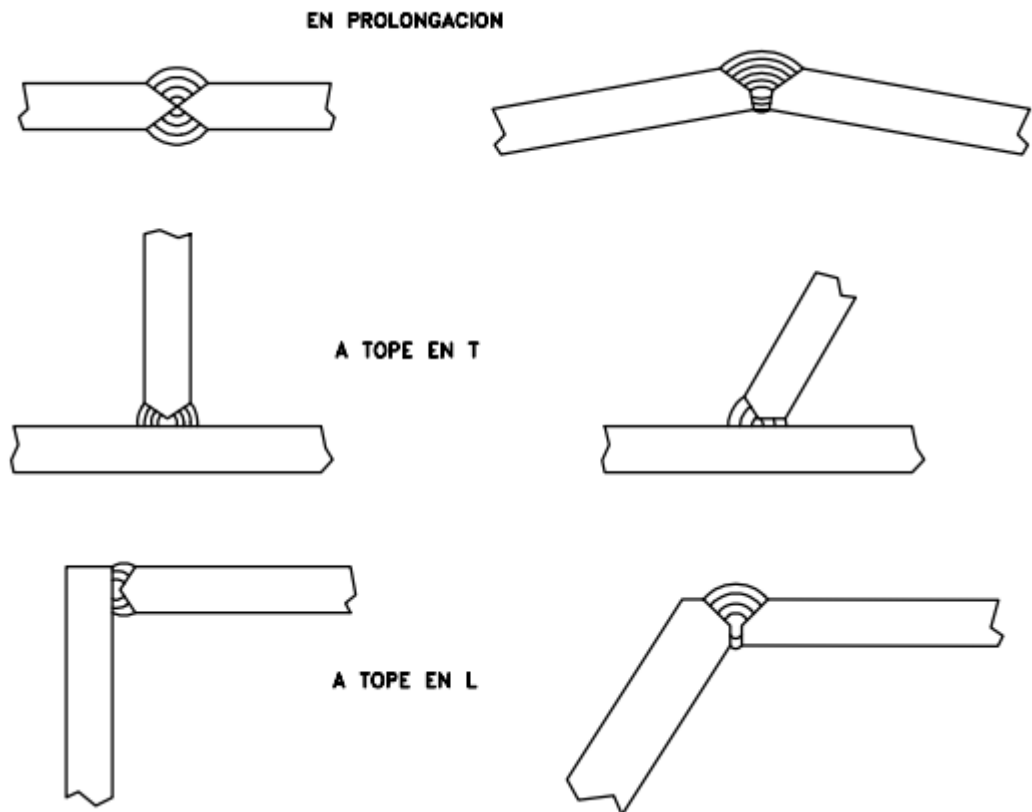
Soldadures a tope (Font: Universidad de Castilla la Mancha)
